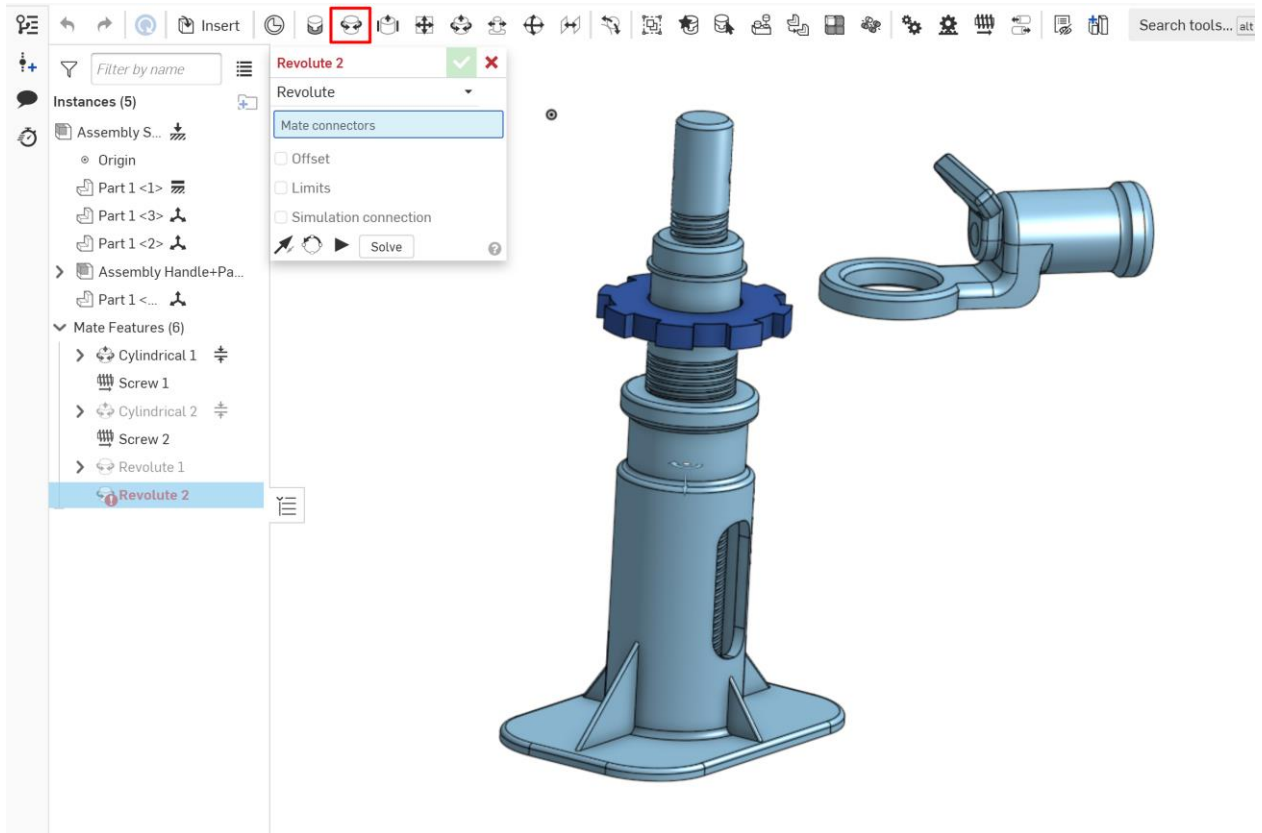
Використання сполучення revolute mate для приводного важеля з собачкой і сопряження fastened mate для храпового колеса
